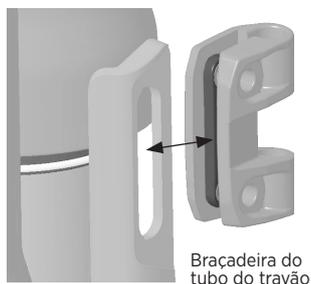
Instalação da braçadeira do tubo do travão no mastro
